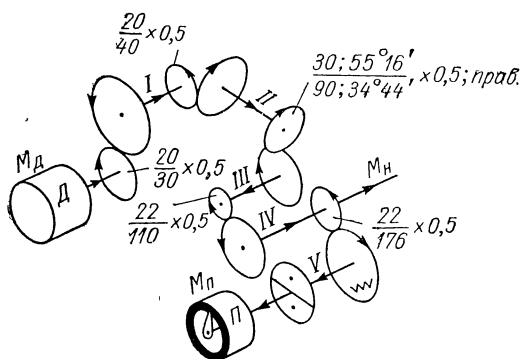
Кинематическая схема редуктора приборной следящей системы
